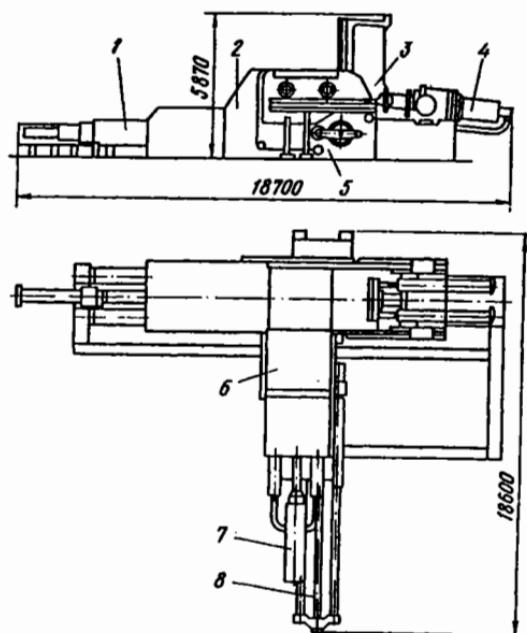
Пакетировочный гидравлический пресс Б 1642
